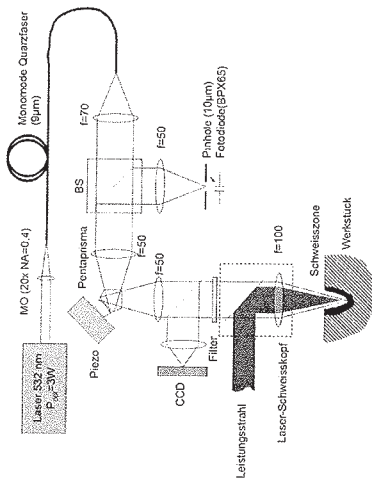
Aufbau des Keyholesensors mit Piezo-Aktor.
